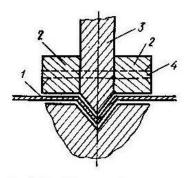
Приспособление для изготовления профилированных панелей на кромкогибочном станке:
